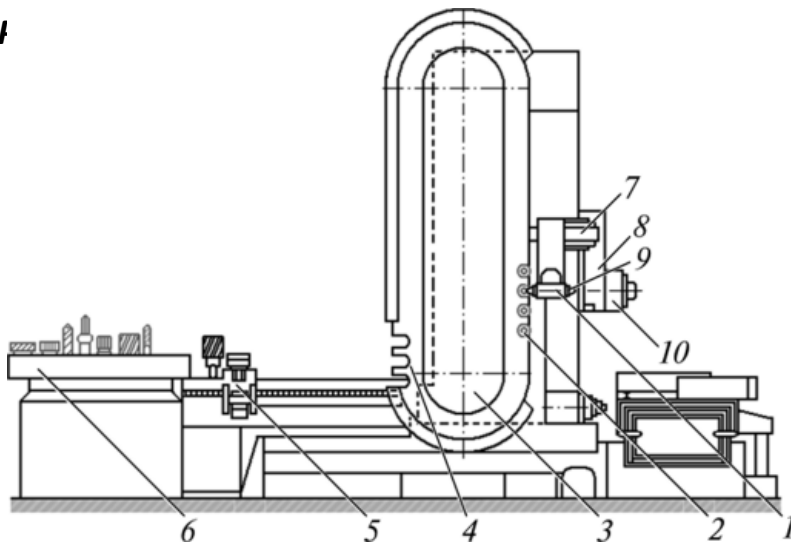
Схема устройства АСИ с перемещающимся между магазином и шпинделем автооператором:
